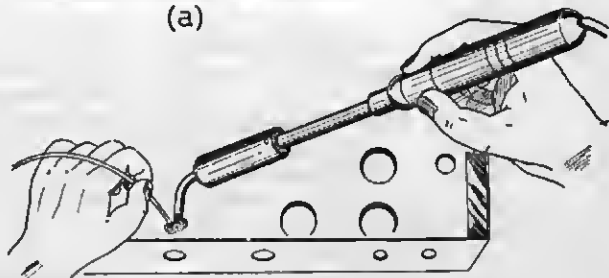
Soldadura de una conexión sobre el chasis: (a) Detalle de la soldadura terminada.
